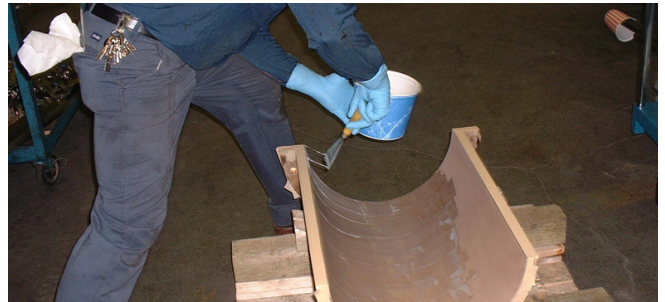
Adhesivo siendo aplicado a una carcasa metálica dividida
